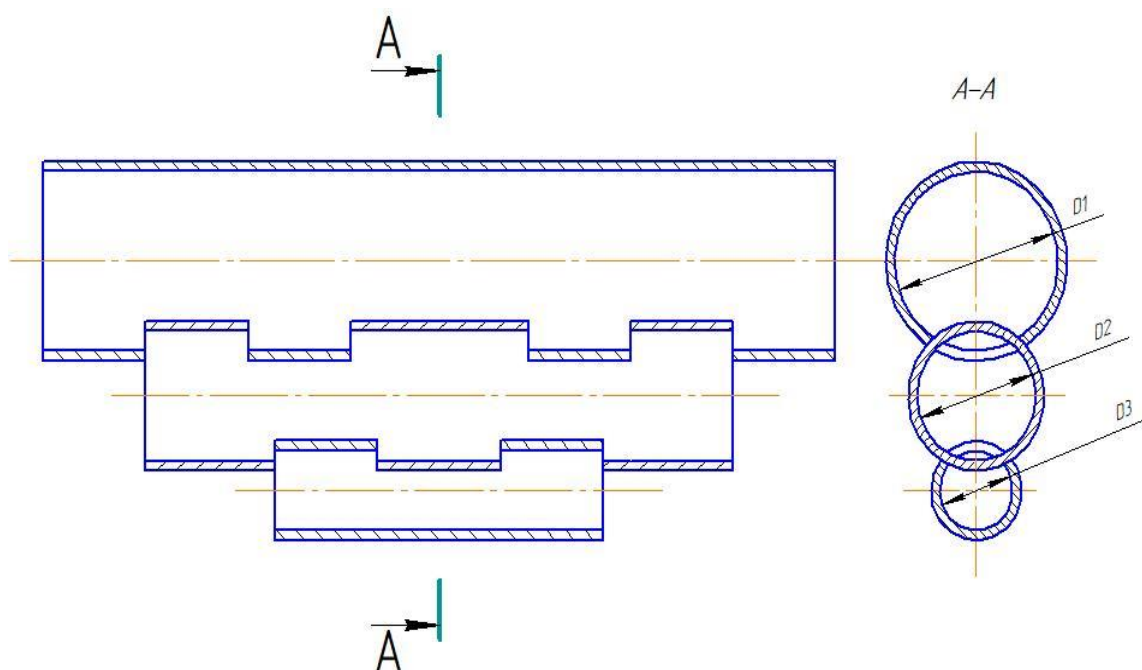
Схема расположения труб главной балке (Патент РФ №2031073)
